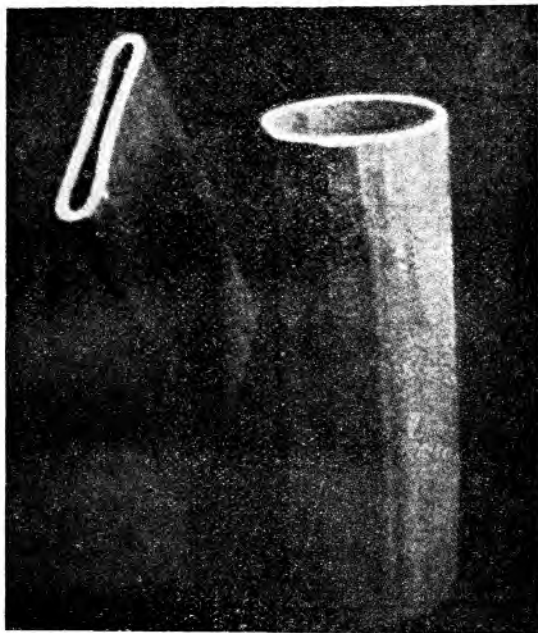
Стальная труба, сжатая после сварки без малейшего излома или трещины по линии сварки. Пламя атомного водорода позволяет сваривать и другие металлы, как, например, медь и сталь, медь и инвар, или сваривать различные сорта стали.
